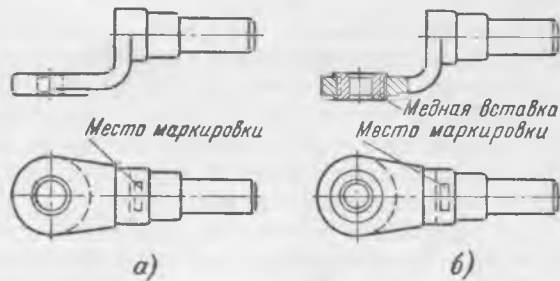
Литые алюминиевые наконечники типа ЛА в исполнении для сварки.
